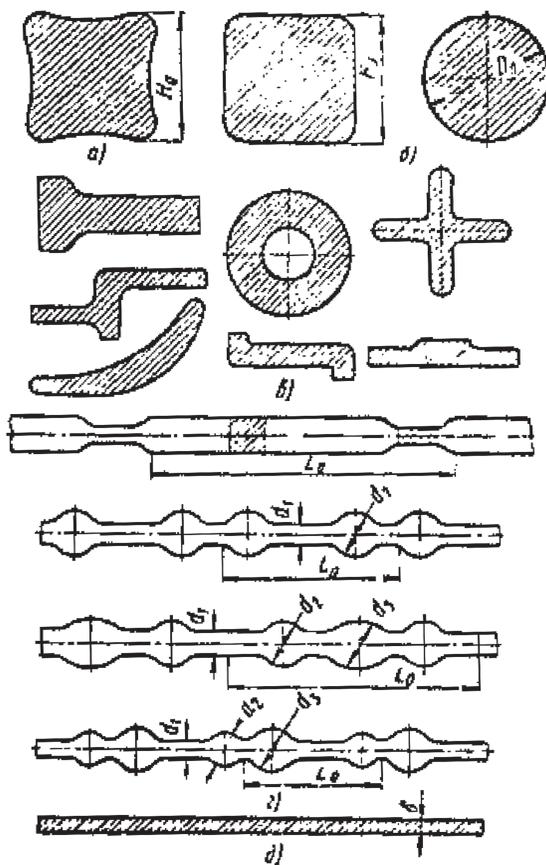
Типы прокатных профилей дляковки и штамповки:
